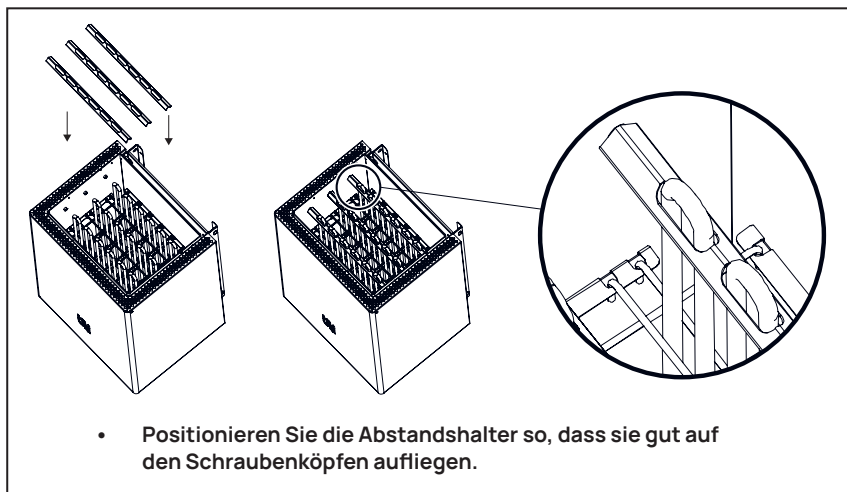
Installation des HUUM CORE Wall und CORE Wall Combi Heizelement-Abstandhalters.
